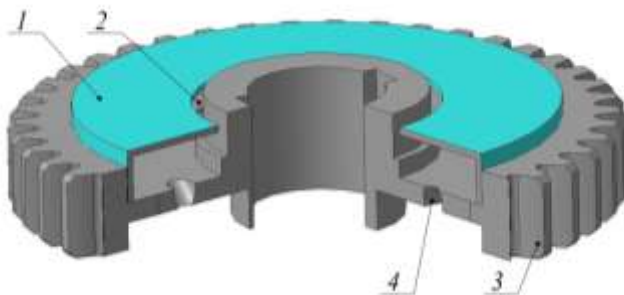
Предлагаемая конструкция шестерни, в полости которой закреплена цилиндрическая вставка
